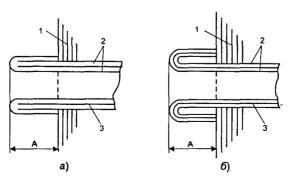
Расположение пазовой коробочки в пазу и вылет манжеты: a — манжета, образованная внутренним слоем пазовой коробочки, δ — манжета, образованная тремя слоями пазовой коробочки; 1 — пакет железа, 2 — электрокартон, 3 — внутренний слой лакоткани или миканита
